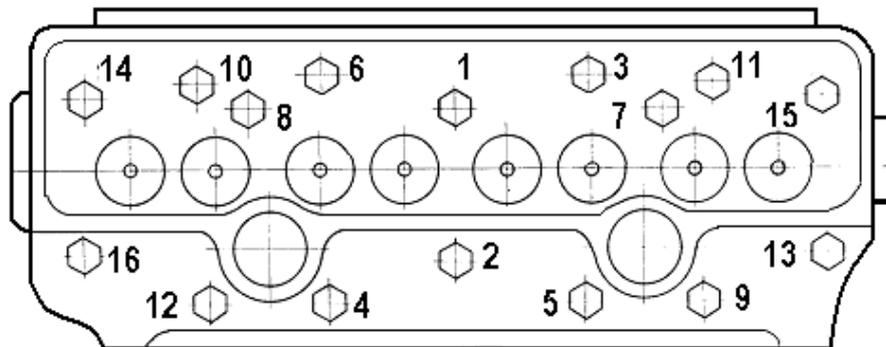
Схема последовательности затяжки болтов крепления головки цилиндров
